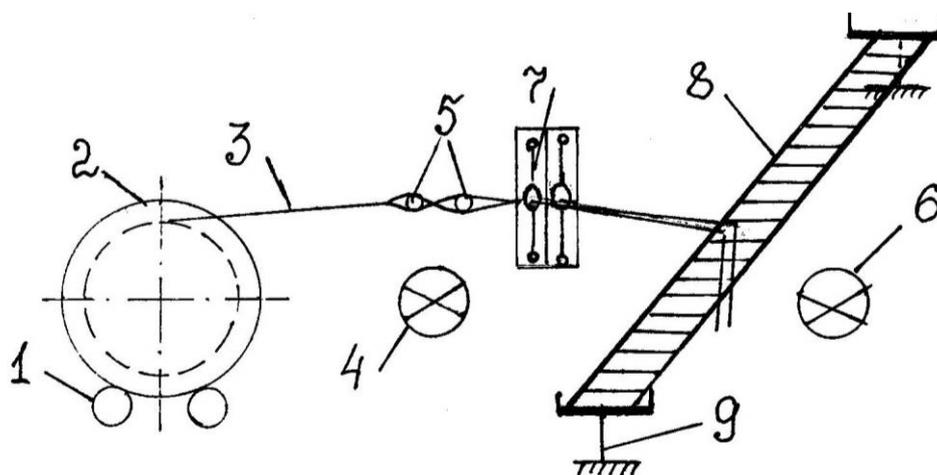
Схема заправки нитей на проборном станке ПС-180
